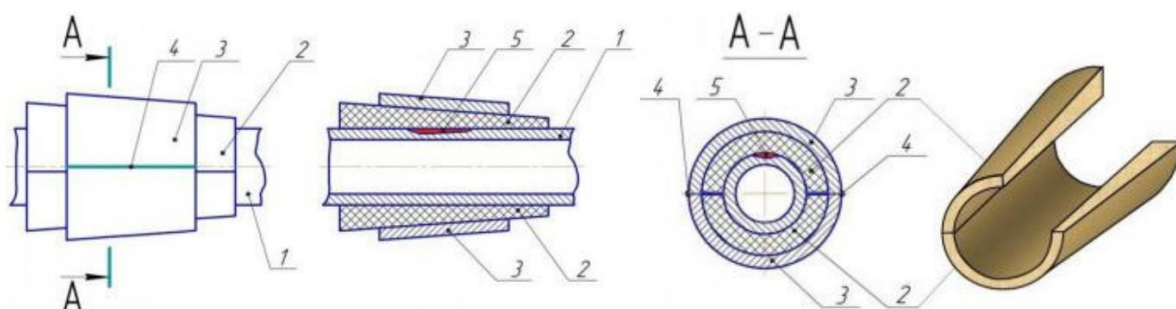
Конструкция муфты КОНУС 1 – трубопровод; 2 – композиционная муфта; 3 – стальная обечайка; 4 – сварной шов; 5 – несквозной дефект [12]
